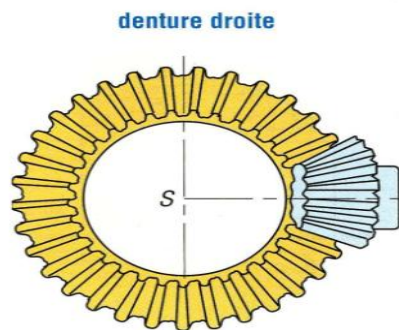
Engrenage conique ou à axes concourants [1].
